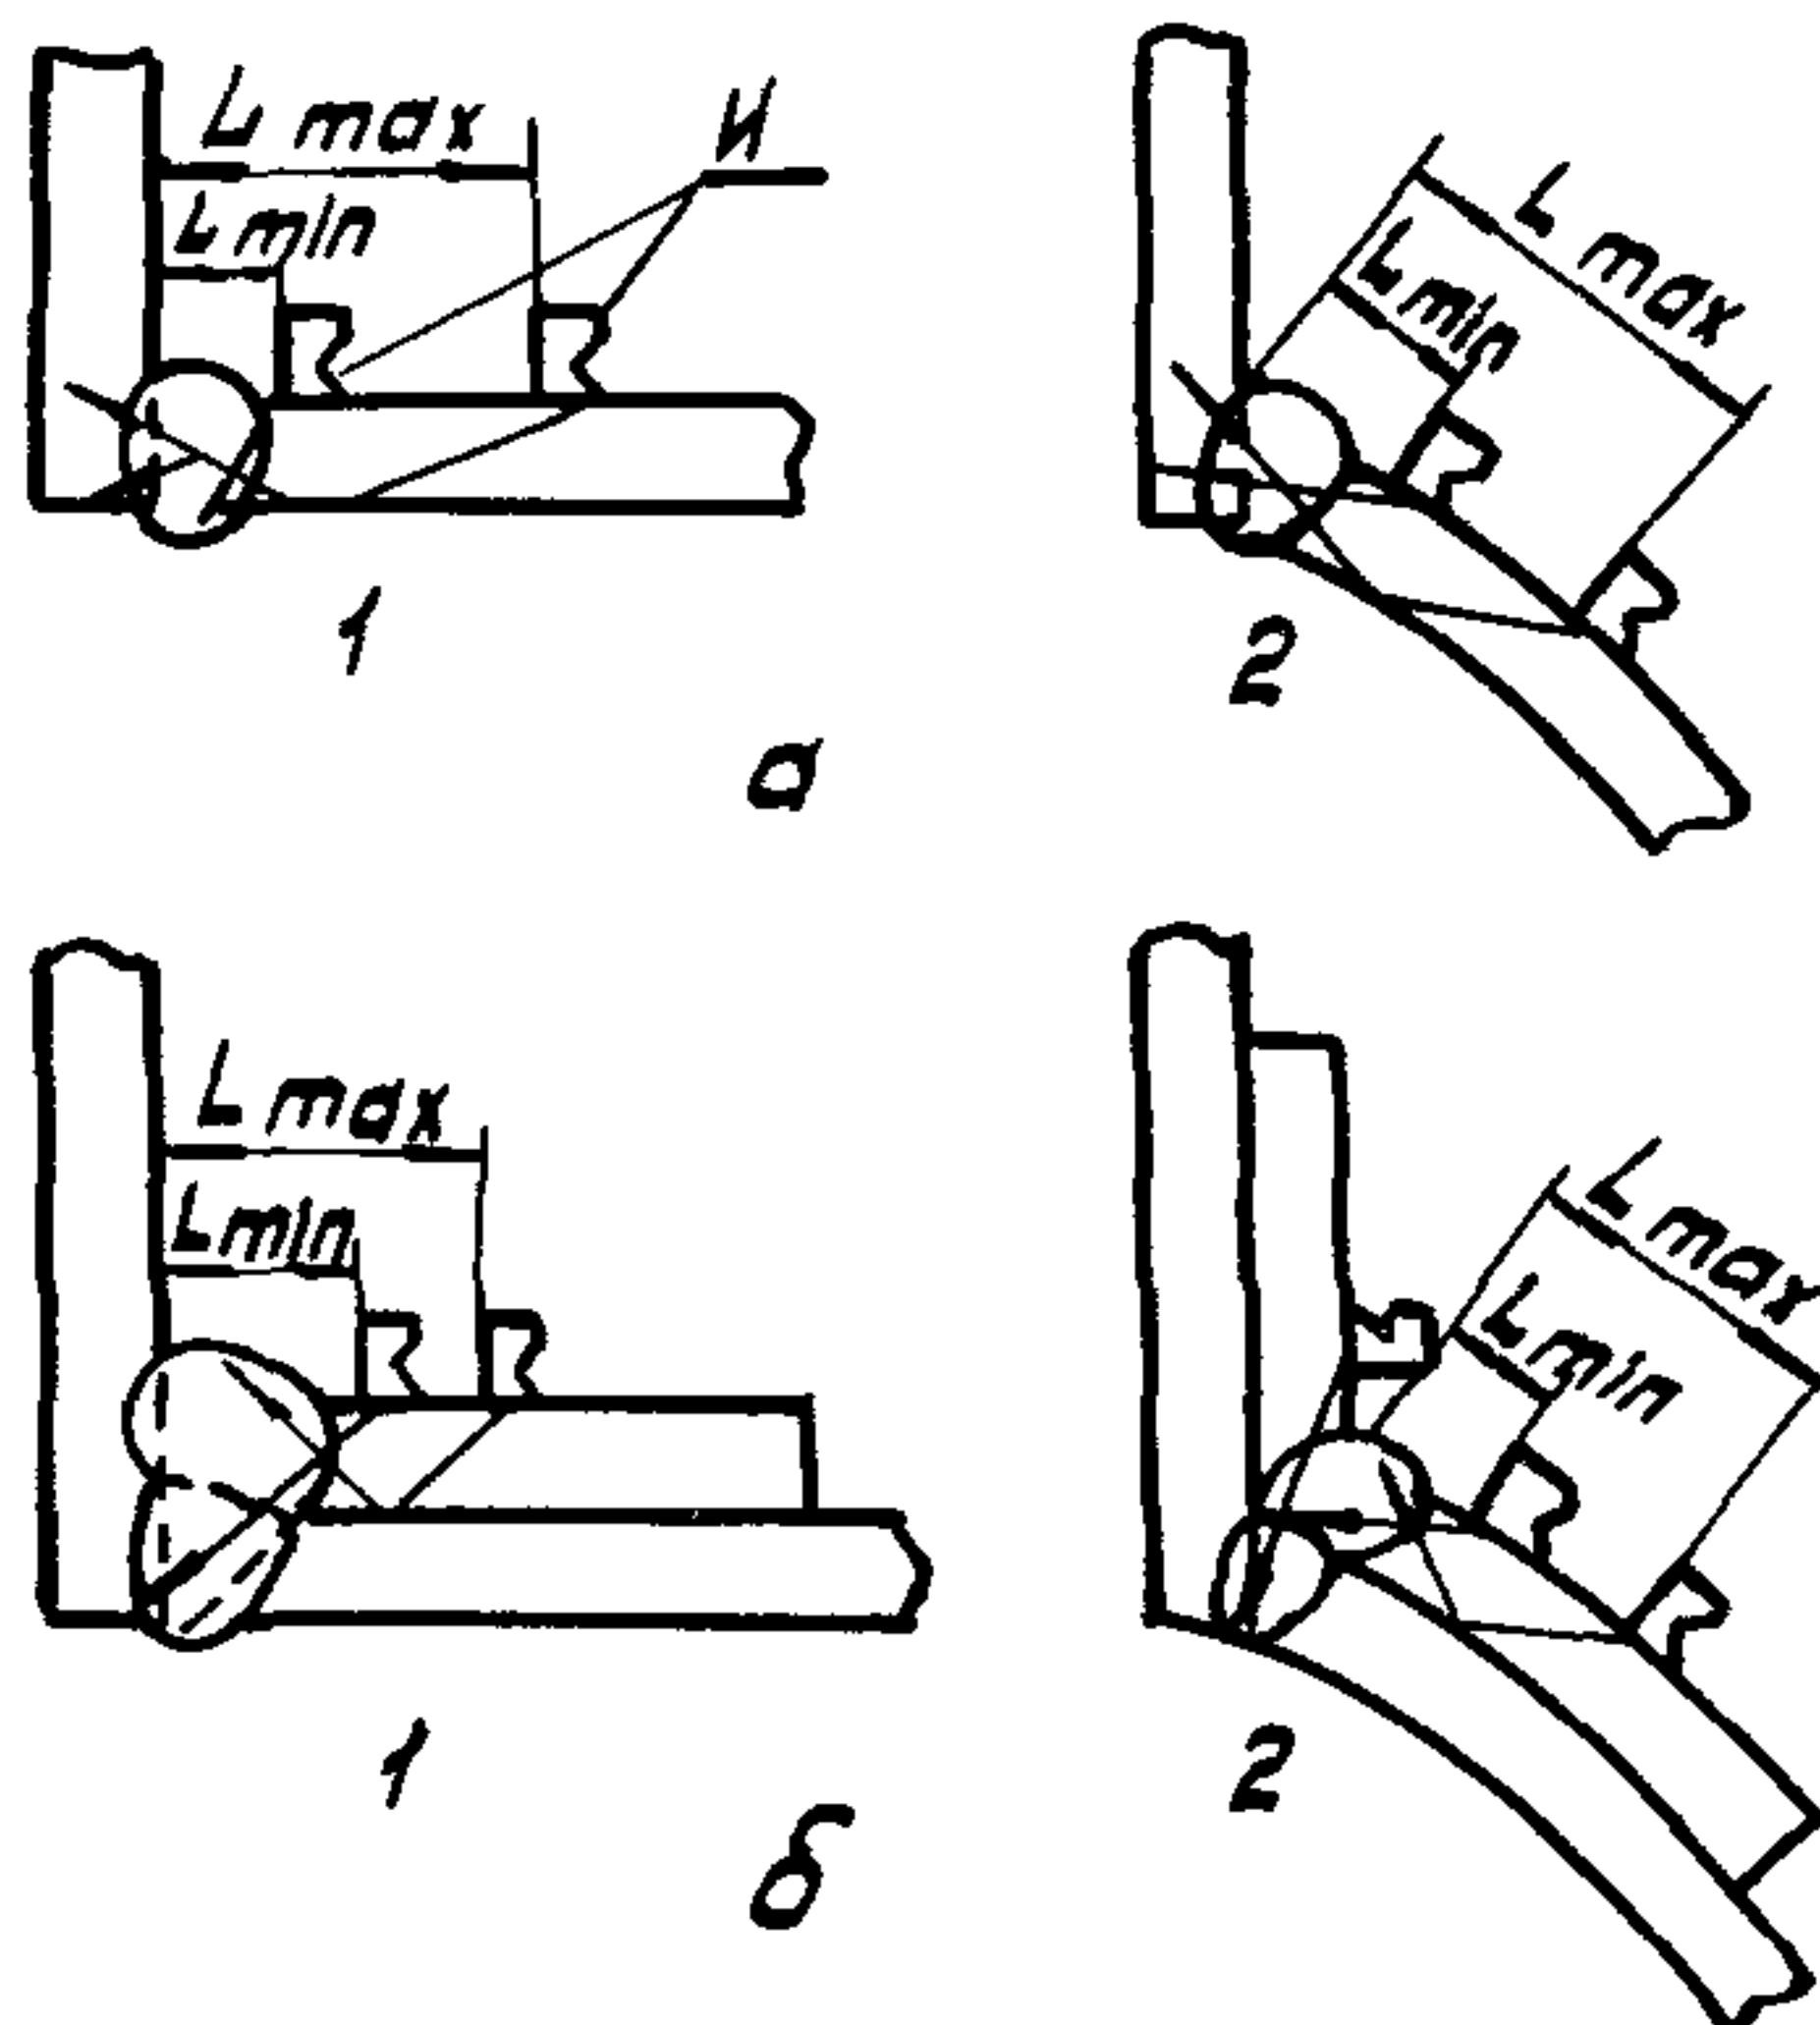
Схемы прозвучивания угловых сварных соединений пленок:
